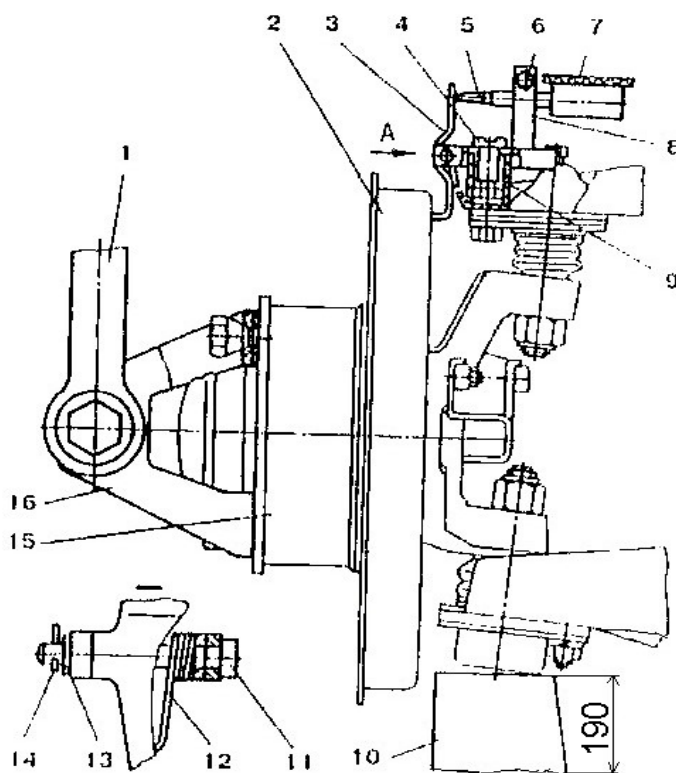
Замер зазора в верхнем шаровом шарнире проверяется приспособлением № 02.8701.9500
